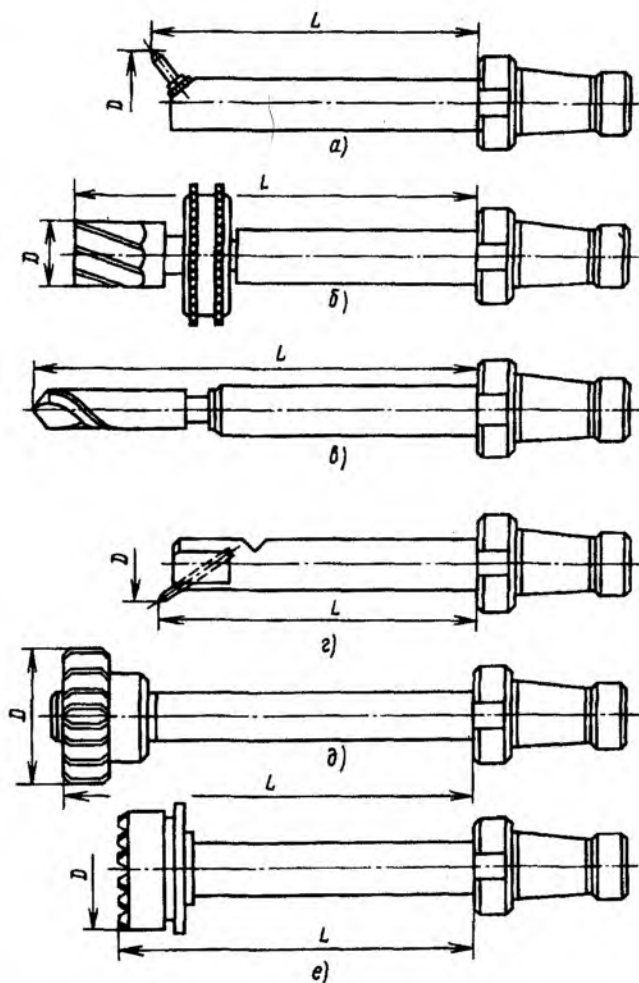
Инструмент, используемый на расточных станках с ЧПУ
